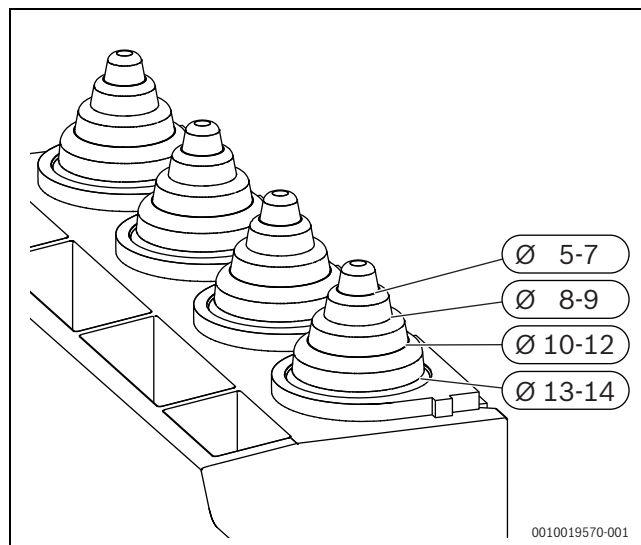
Zugentlastung an Kabeldurchmesser anpassen
